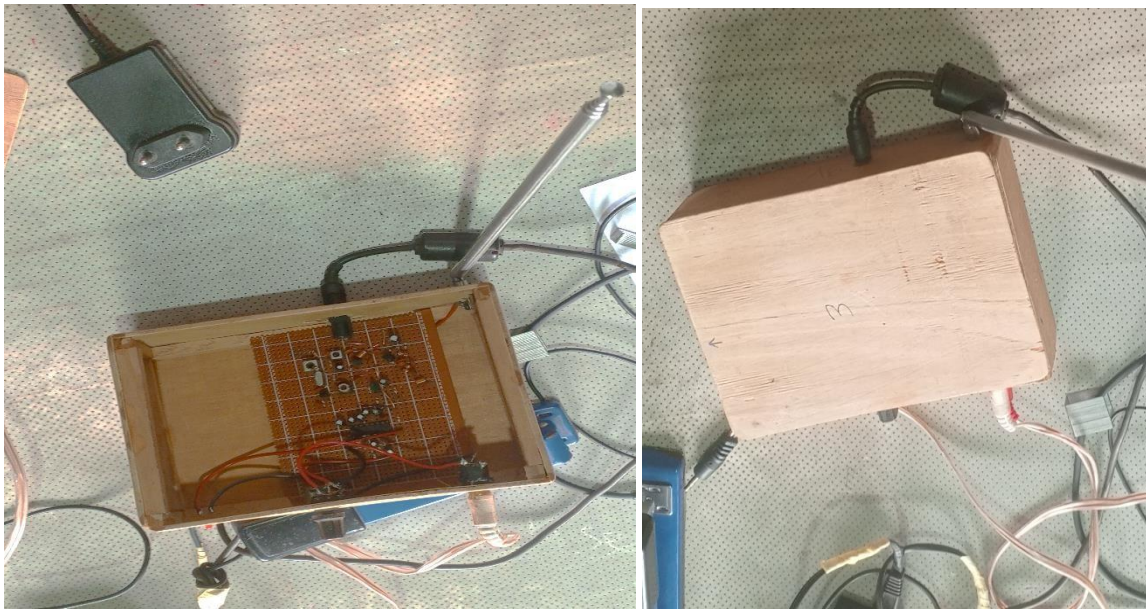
Le montage de l'émetteur par soudure avec fer à souder et étain
